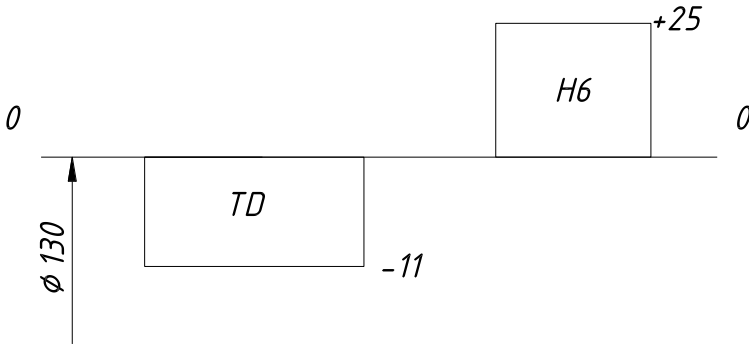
Схема розташування полів допусків корпусу і зовнішнього кільця підшипника
